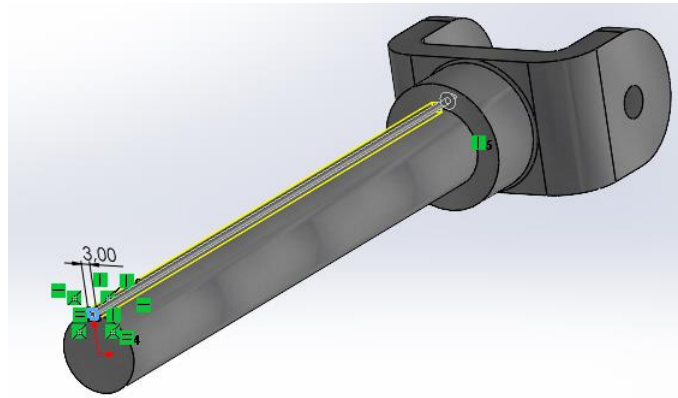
Extrusión árbol de transmisión fijo de la junta cardán en SolidWorks.
